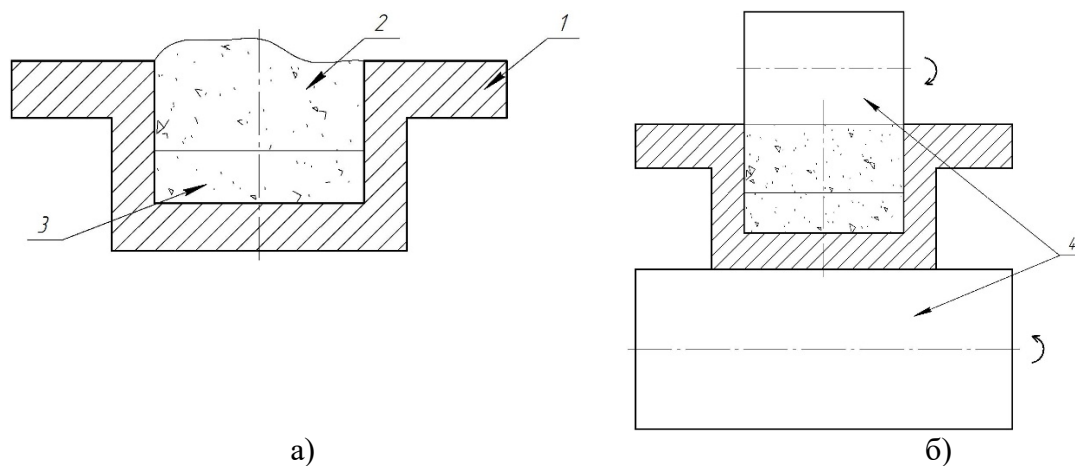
Схема прокатки двух слоёв порошка в металлической П-образной оболочке
